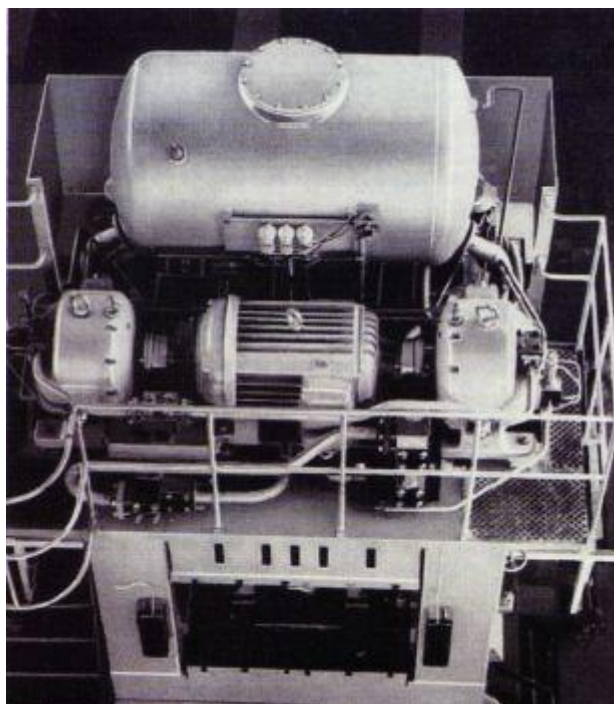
Гидравлический привод листоштамповочного прессы.
